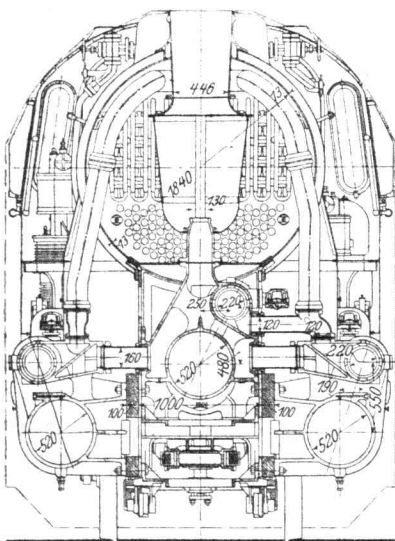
Querschnitt durch die 3 Dampfzylinder.
